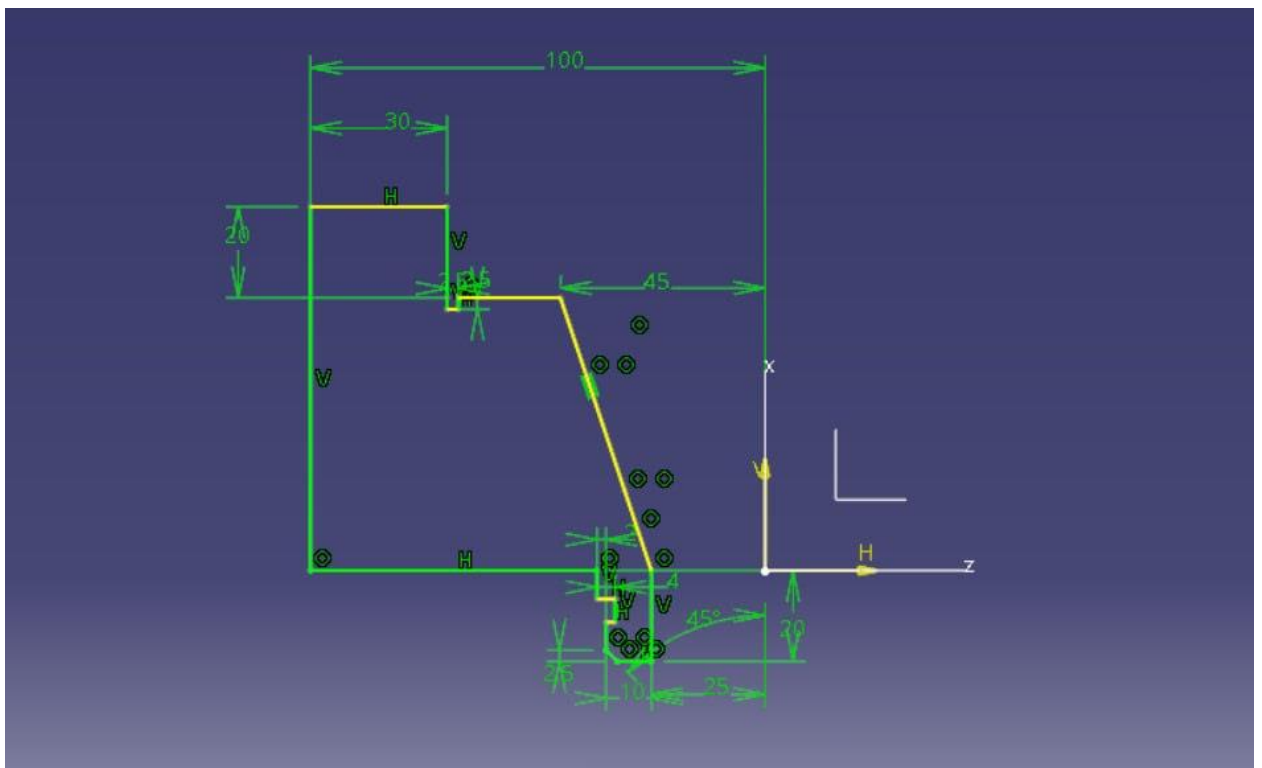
Ескіз деталі фігури для обертання
